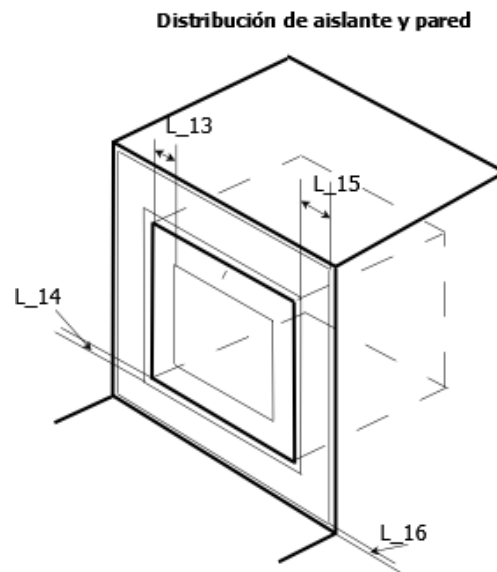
Esquema con cotas del dimensionamiento de capas de aislante de la sección del horno.
